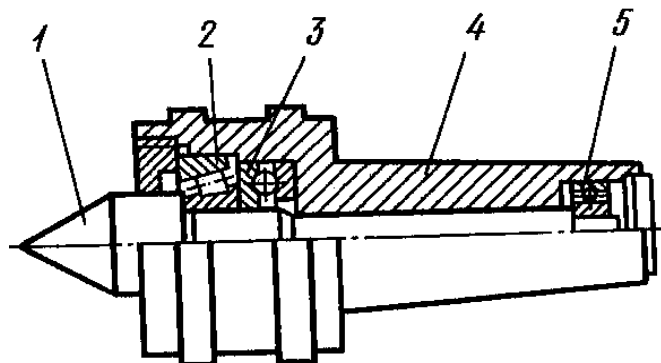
Центр станочный вращающийся: 1 – рабочая часть; 2, 3 и 5 – подшипники; 4 хвостовая часть
